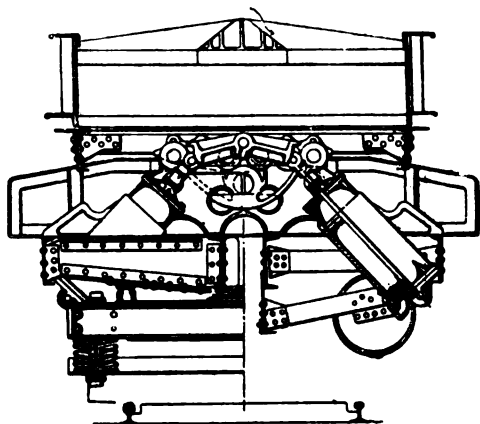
e 18. — Carro a scarico rapido. — Elevazione e sezione trasversale.
